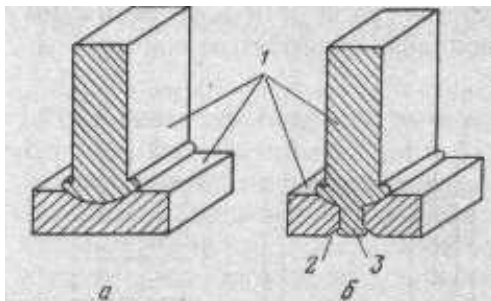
Сварка по схеме «с преимущественным оплавлением»: а – без принудительного затекания материала; б – с принудительным затеканием расплавленного материала; 1 – свариваемые детали; 2 – фаска; 3 – расплавленный материал
